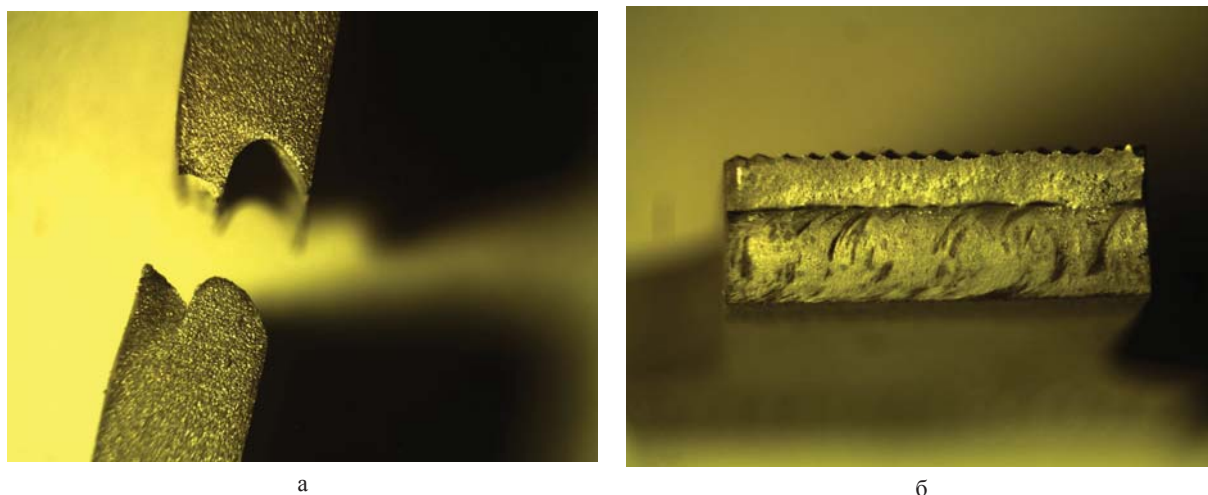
Разрушенный образец со сварным соединением (режим 3): а — вид сверху; б — вид сбоку
